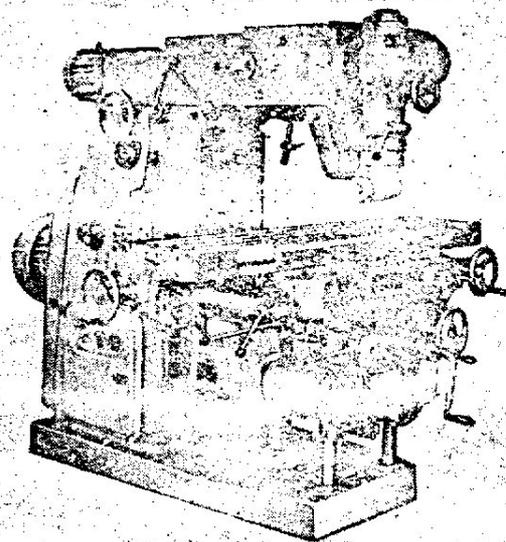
а. Широкоуниверсальный консольно-фрезерный станок модели 6М83Ш
